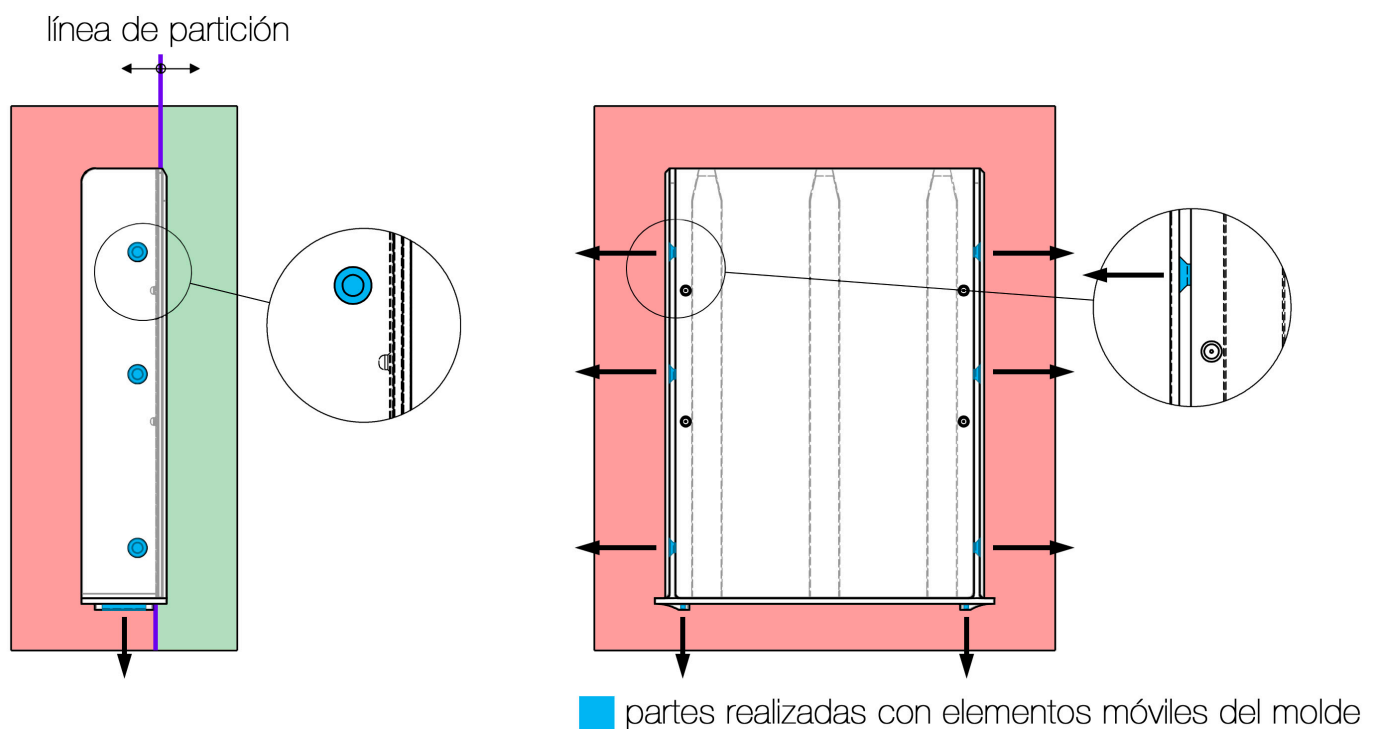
mitades molde pieza "6.4.2.- Adaptador"
